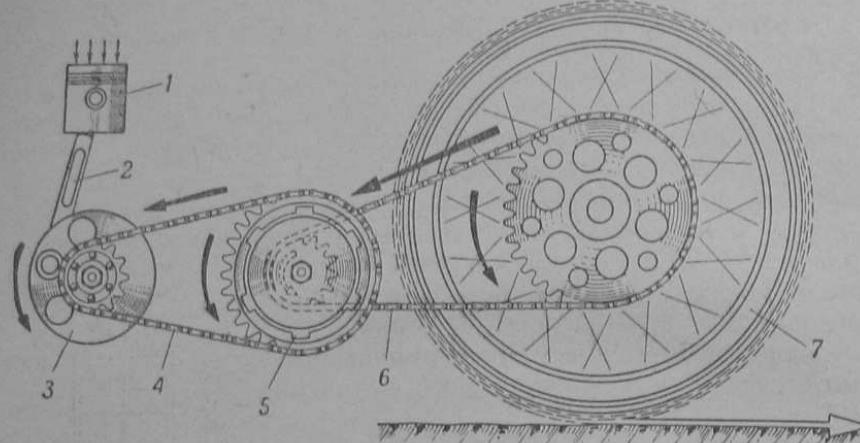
Схема передачи усилия от кривошипного механизма к ведущему колесу:
